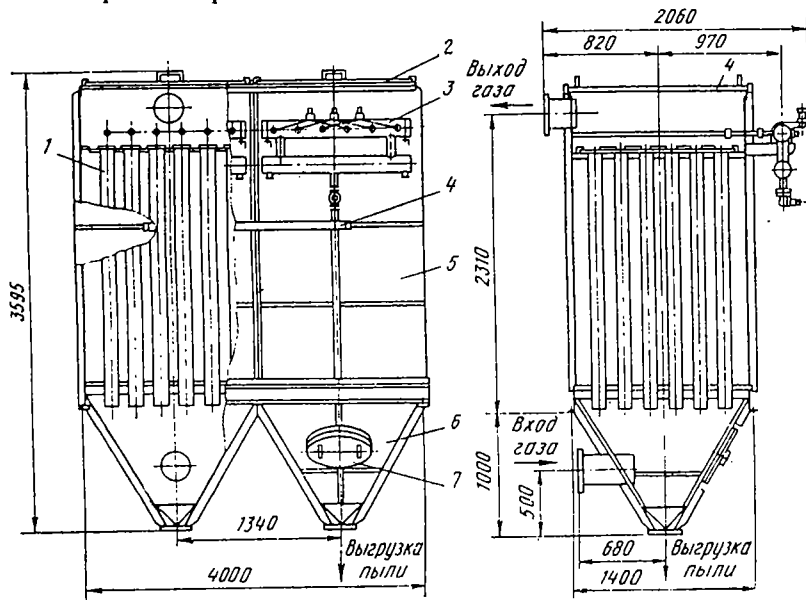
Конструкция рукавного фильтра типа ФРКИ:
